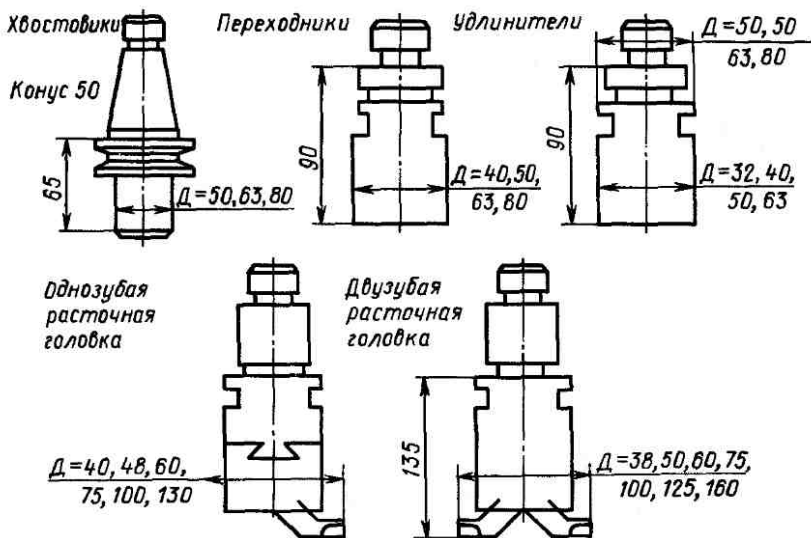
Модульные конструкции одно- и двухзубого расточного инструмента
